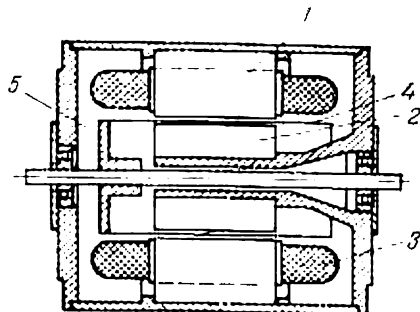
Machine asynchrone diphasée à rotor creux :
